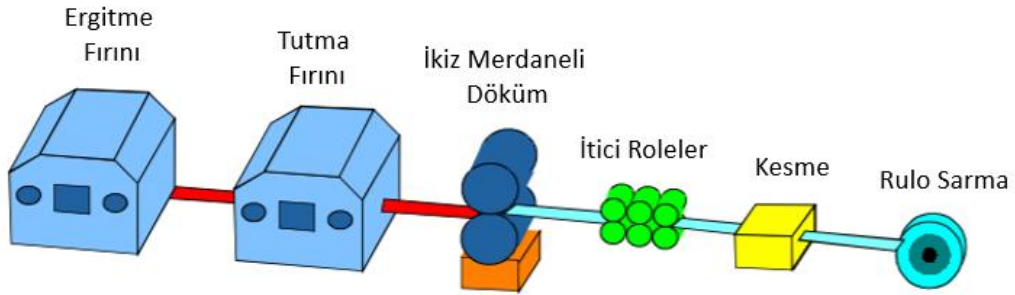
Dikey yukarı doğru Hunter döküm makinası [21].
